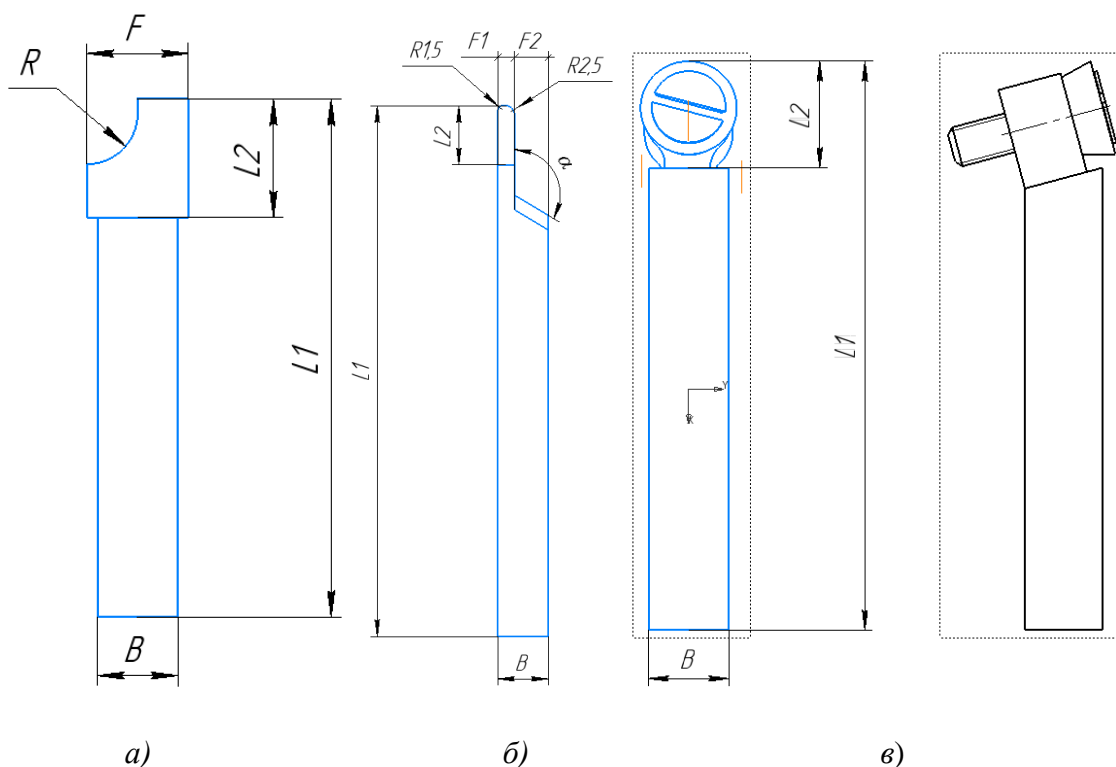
Конструкция фасонных резцов: *а* – стержневой, для обработки наружных шаровых и сферических поверхностей; *б* – стержневой, для обработки наружных фасонных канавок; *в* – резец с круглой сменной пластиной.
